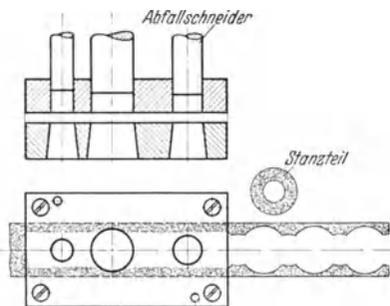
Schnittwerkzeug mit Streifenrenner.
